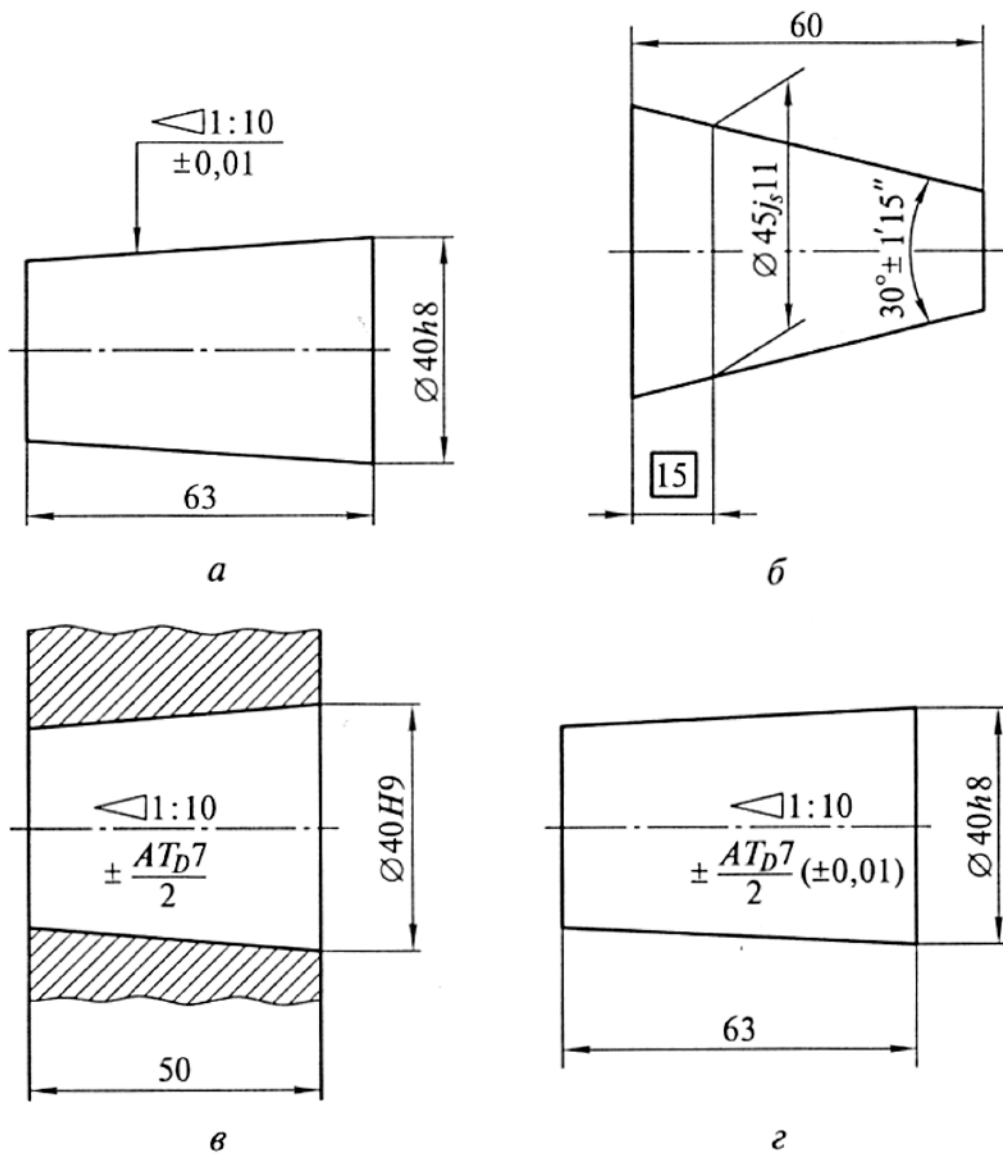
Числовой (а, б), условный (в) и смешанный (г) способы обозначения допусков конусов на чертежах
